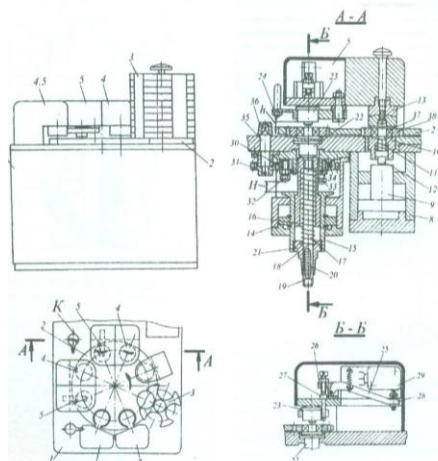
Конструкция полуавтомата для засекания подшипников в сателлиты планетарных редукторов.
